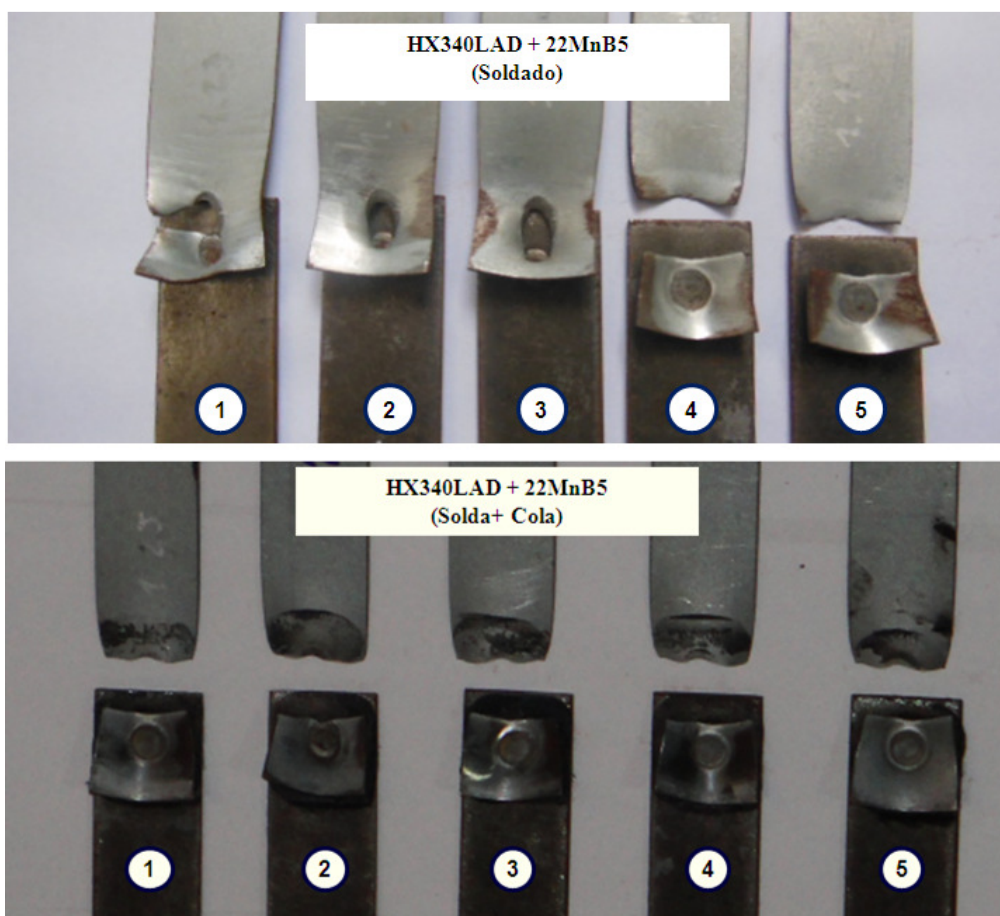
Detalhe das uniões soldadas rompidas HX340LAD + 22MnB5.
